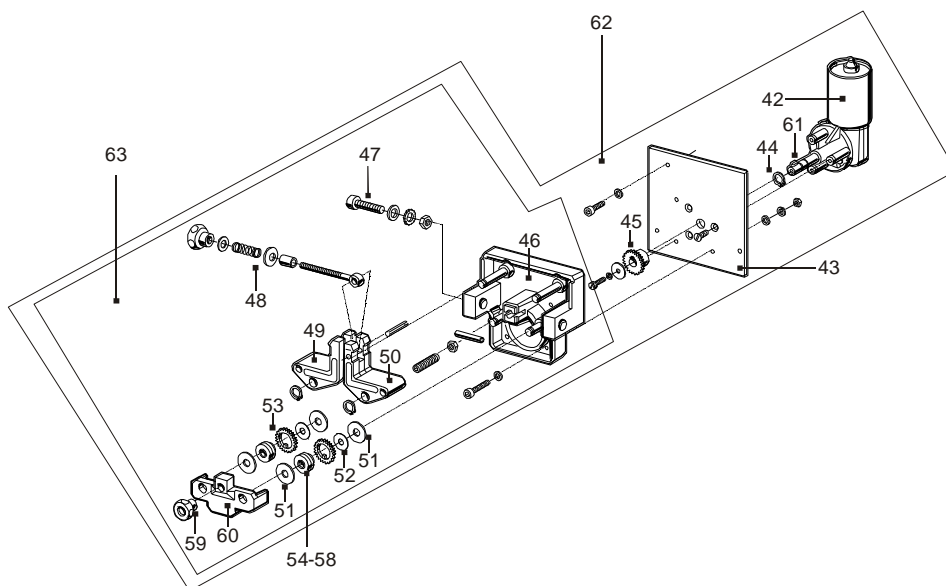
Explosionszeichnung 4-Rollen-Antrieb
